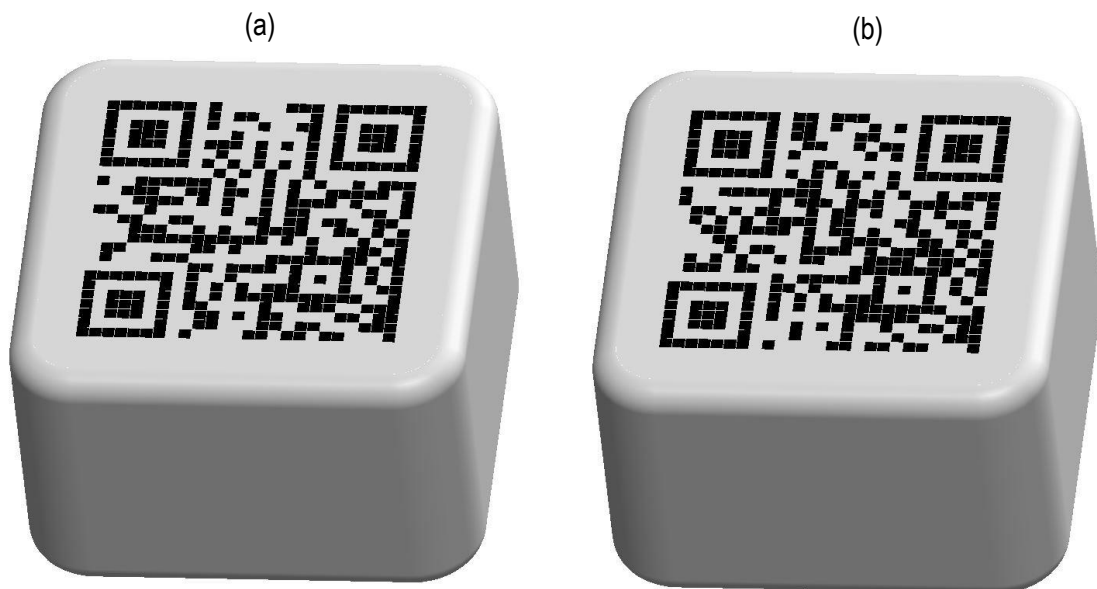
Pieza a procesar con Código QR (a) Pieza A; (b) Pieza B
